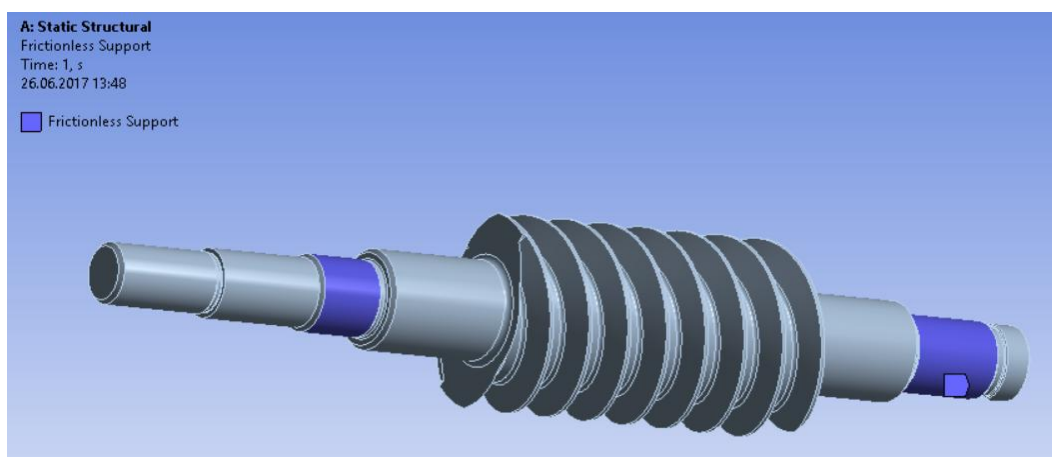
3D модель вала червячной передачи в ANSYS.
